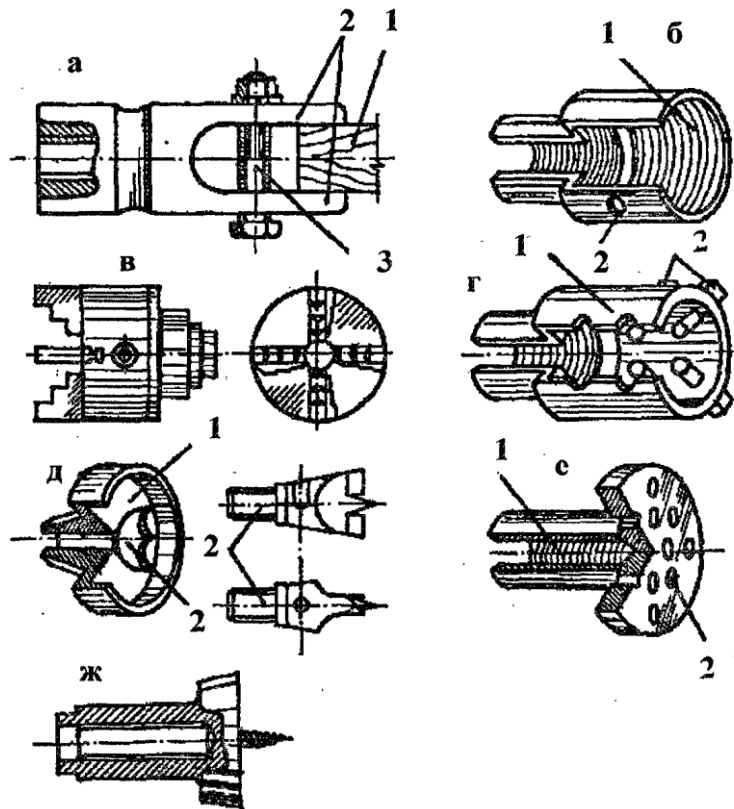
Затискні патрони для точіння деревини: а – лещатний патрон (1 – заготовка; 2 – губки лещат; 3 – кріпильний гвинт); б – трубчастий патрон (1 – металевий стакан; 2 – кріпильні гвинти); д – патрон-тризубець (1 – металевий стакан з різьбленням; 2 – утримувачі гребенеподібного і циліндрового лещат); е – планшайба (1 – утримувач з різьбою; 2 – отвір для фіксатора); в – чотирьохкулачковий патрон; г – чашковий патрон (1–2 – кріпильні отвори); ж – патрон з конічним гвинтом.
